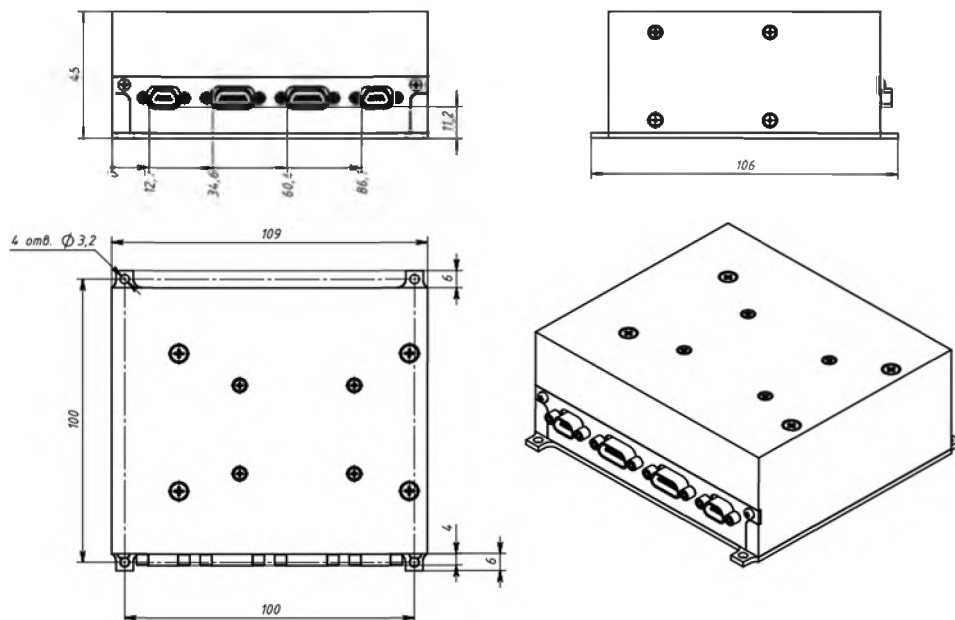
Габаритный чертёж БУСОС SX-ADCSCU-02
